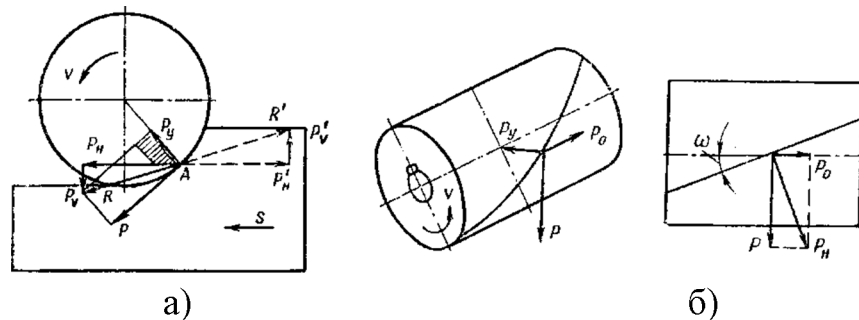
Силы резания при работе цилиндрической фрезой
